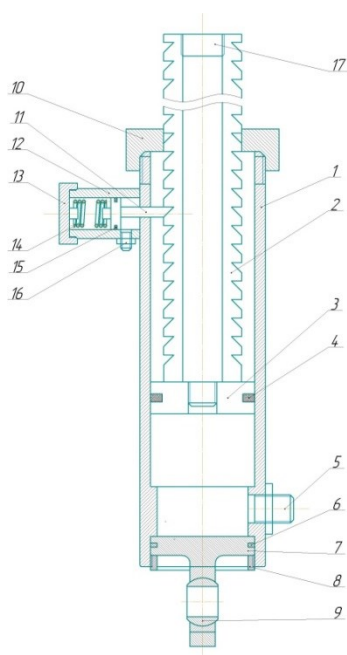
Гидравлический цилиндр: 1 – корпус; 2 – шток с прорезями для фиксаторов; 3 – поршень; 4 – уплотнения; 5 – штуцер, 6 – уплотнения; 7 – узла крепления; 8 – фасонная шайба; 9 – сферический шарнир; 10 – крышка; 11 – фиксатора; 12 – корпус фиксатора; 13 – крышка; 14 – пружина; 15 – поршня фиксатора с уплотнениями; 16 – штуцер; 17 – хвостовик
